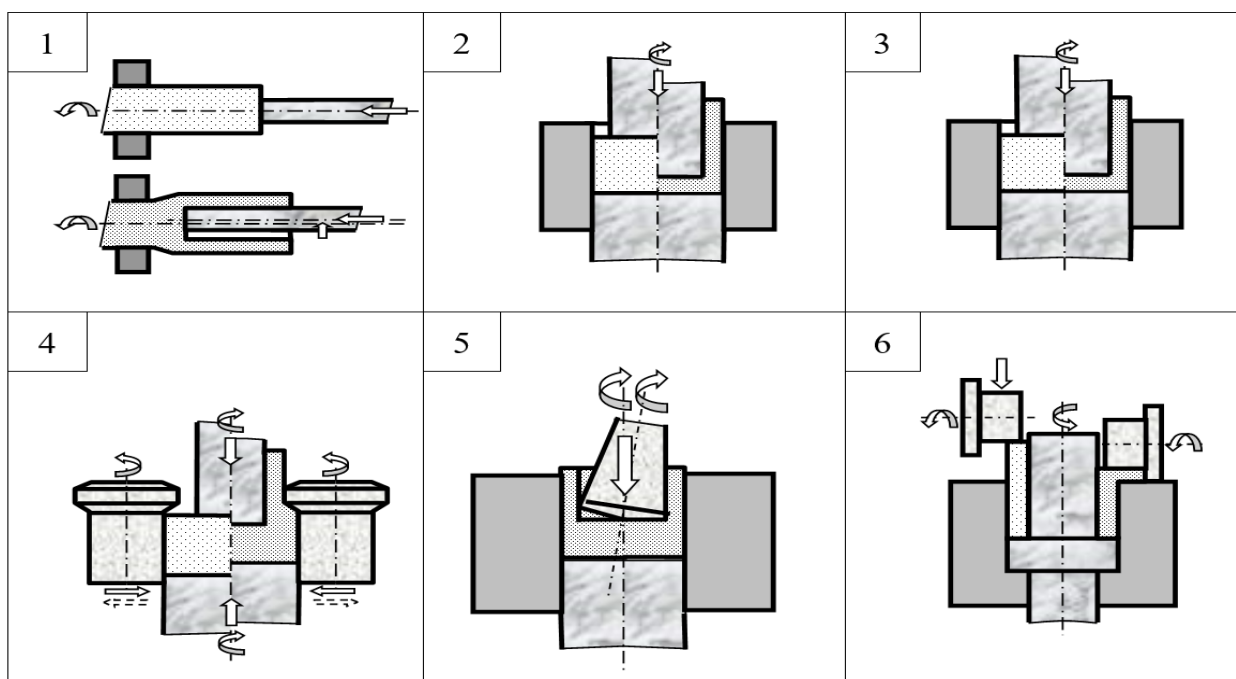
Способи виготовлення прецизійних деталей з різною кінематикою руху інструменту
